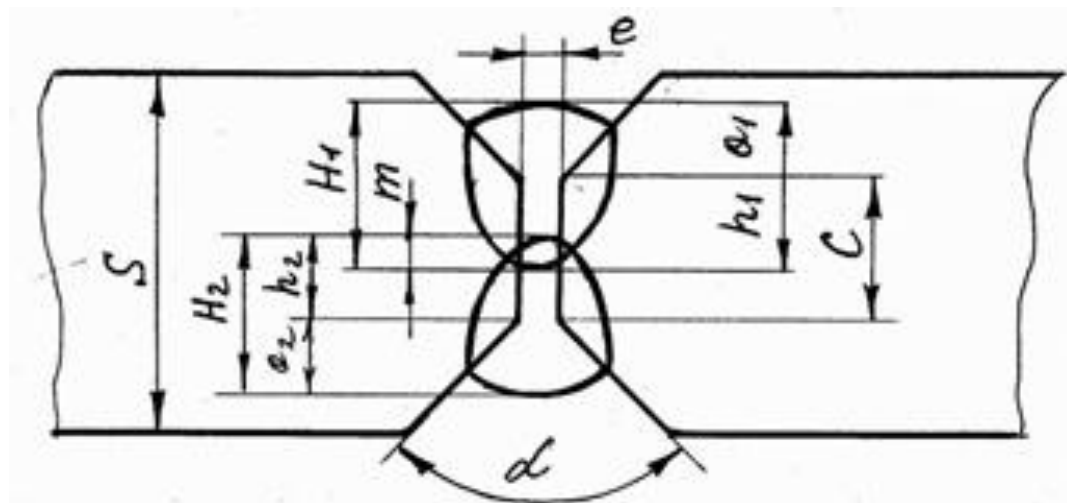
Конструктивні елементи розробки кромки шва при двобічному зварюванні
